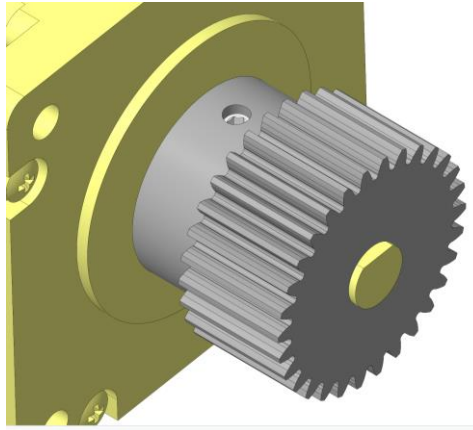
Ozubené kolo modul 1, 30 zubů [51]
